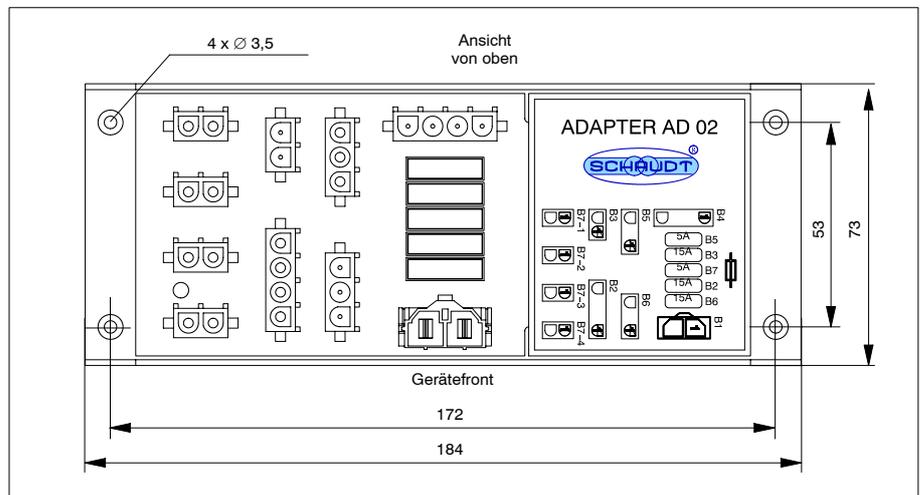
Maßbild Adapter AD 01 und AD 02 (Abmessungen in mm)
